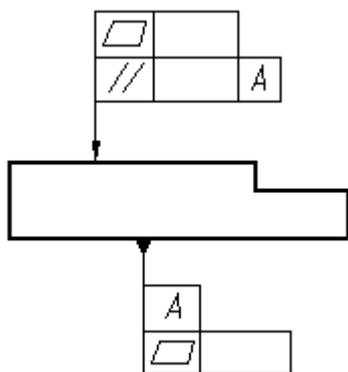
Примеры обозначения двух допусков и буквенного обозначения поверхности с допуском
